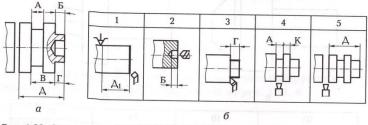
Очередность настройки режущего инструмента на размер: a — эскиз детали;  $\delta$  — схема настройки режущего инструмента
